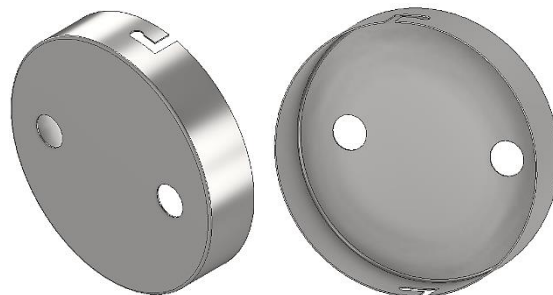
Ukázka výrobků zhotovených tažením [3], [4], [5], [6]
